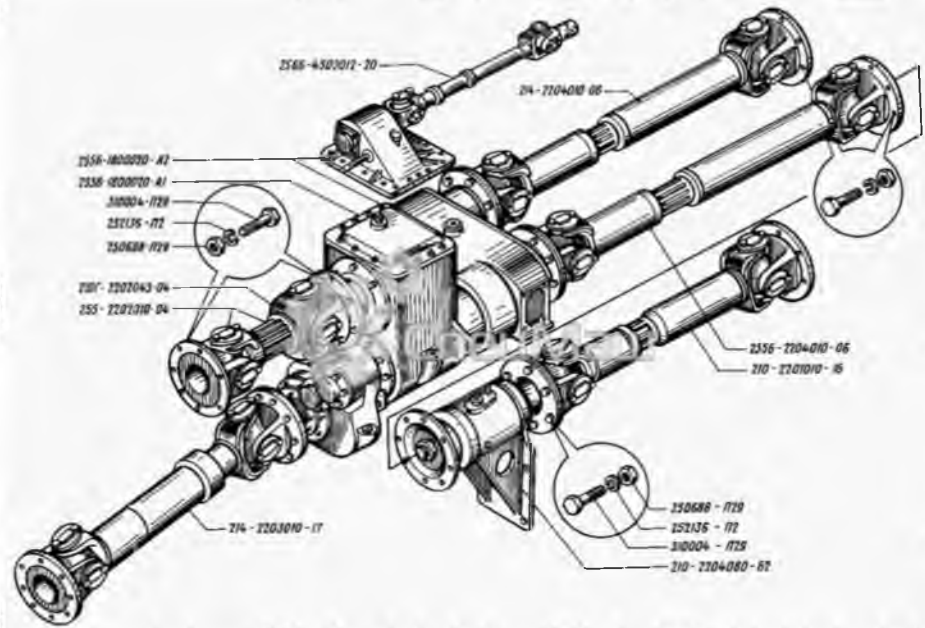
Схема установки вала карданного автомобиля КрАЗ:
